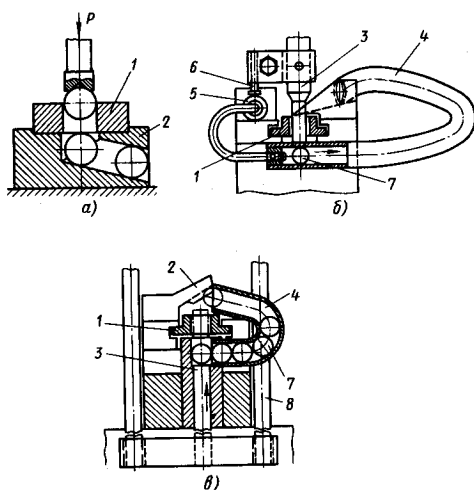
Приспособления для калибрования: а — подставка для калибрования шариком; б — приспособление с пневматической подачей шарика к пуансону; в — приспособление для калибрования снизу вверх; 1 — деталь; 2 — подставка; 3 — пуансон; 4 — труба; 5 — вентиль для сжатого воздуха; 6 — регулируемый упор для автоматического открывания вентиля; 7 — шарик; 8 — тяги, связывающие пуансон с ползуном прессы
